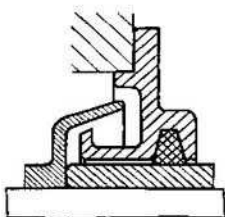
Empaquetadura combinada: disco deflector, guarnición de fieltro
